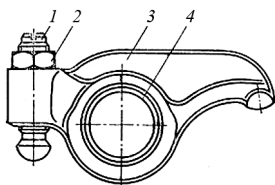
Коромысло ГРМ в сборе: 1 – регулировочный винт; 2 – контргайка; 3 – коромысло; 4 – втулка
